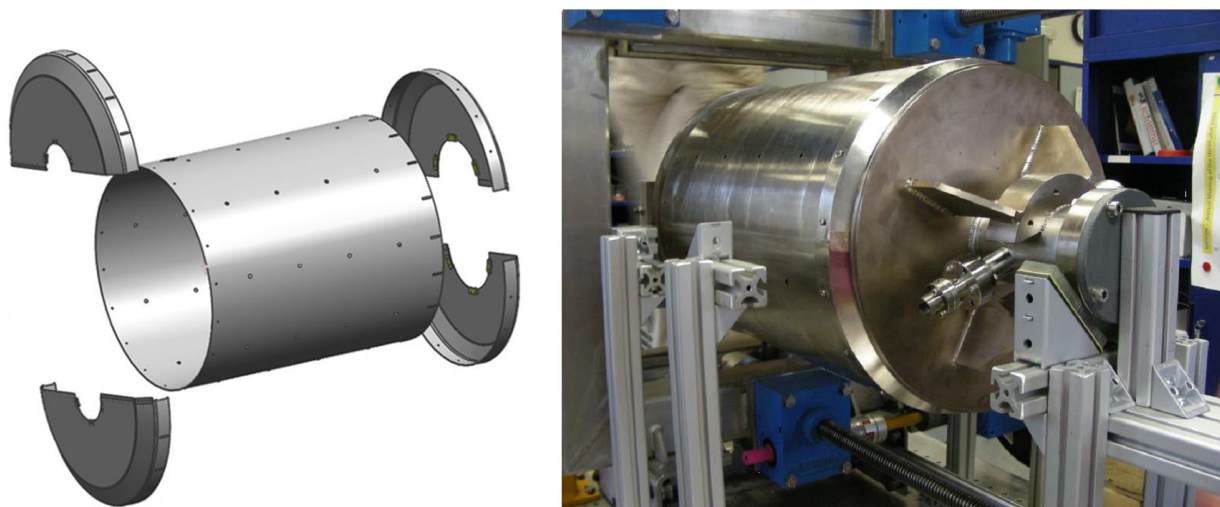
Vue éclatée du blindage magnétique placé dans le tank hélium et positionnement de l'écran durant son assemblage autour de la cavité.
